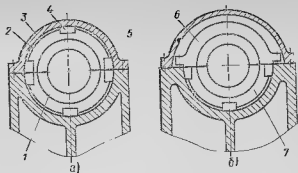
Схемы одноопорного (а) и двухопорного (б) опорных подшипников.
